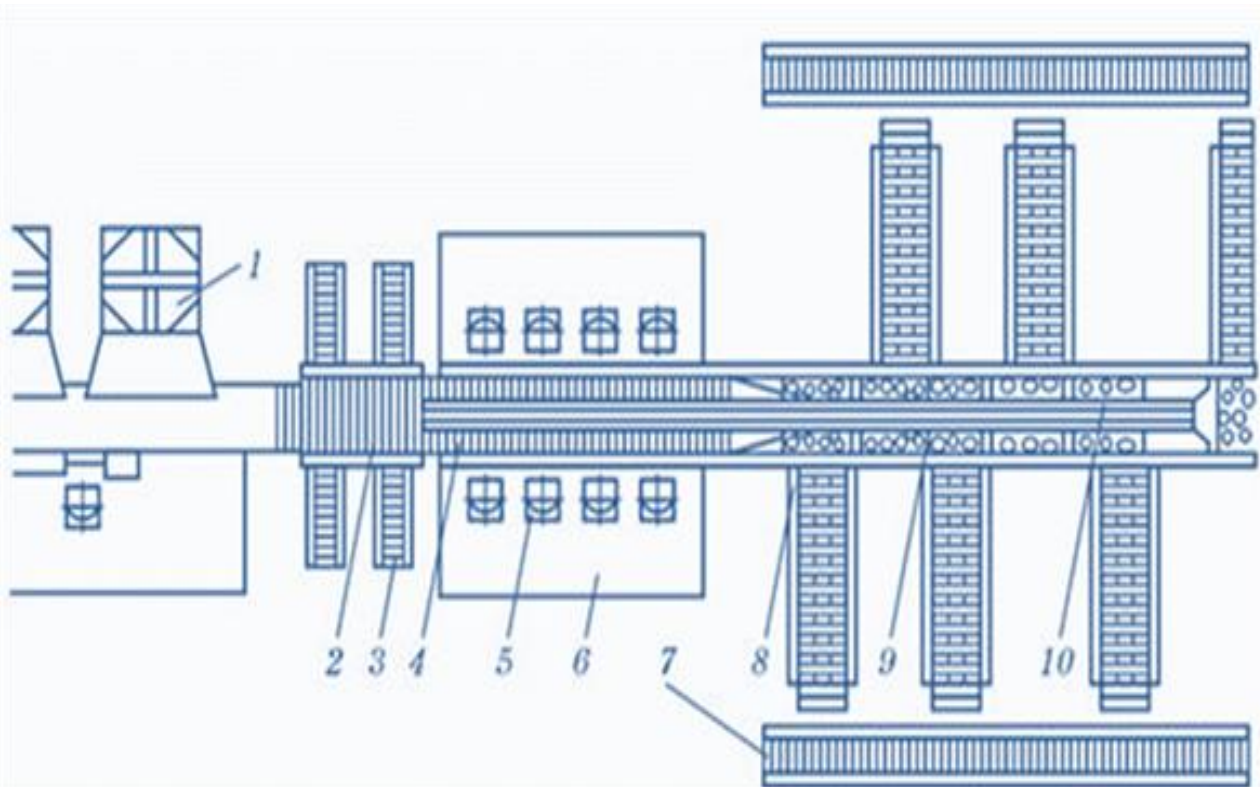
Схема лінії ЛТО-6: 1 – випорожнювач контейнерів; 2 – сепаратор; 3 – рольганг нестандартної продукції; 4 – сортувальний конвеєр; 5 – стілець; 6 – настил; 7 – рольганг; 8 – пакувальний пристрій; 9 – калібрувальний конвеєр; 10 – стрічковий конвеєр
